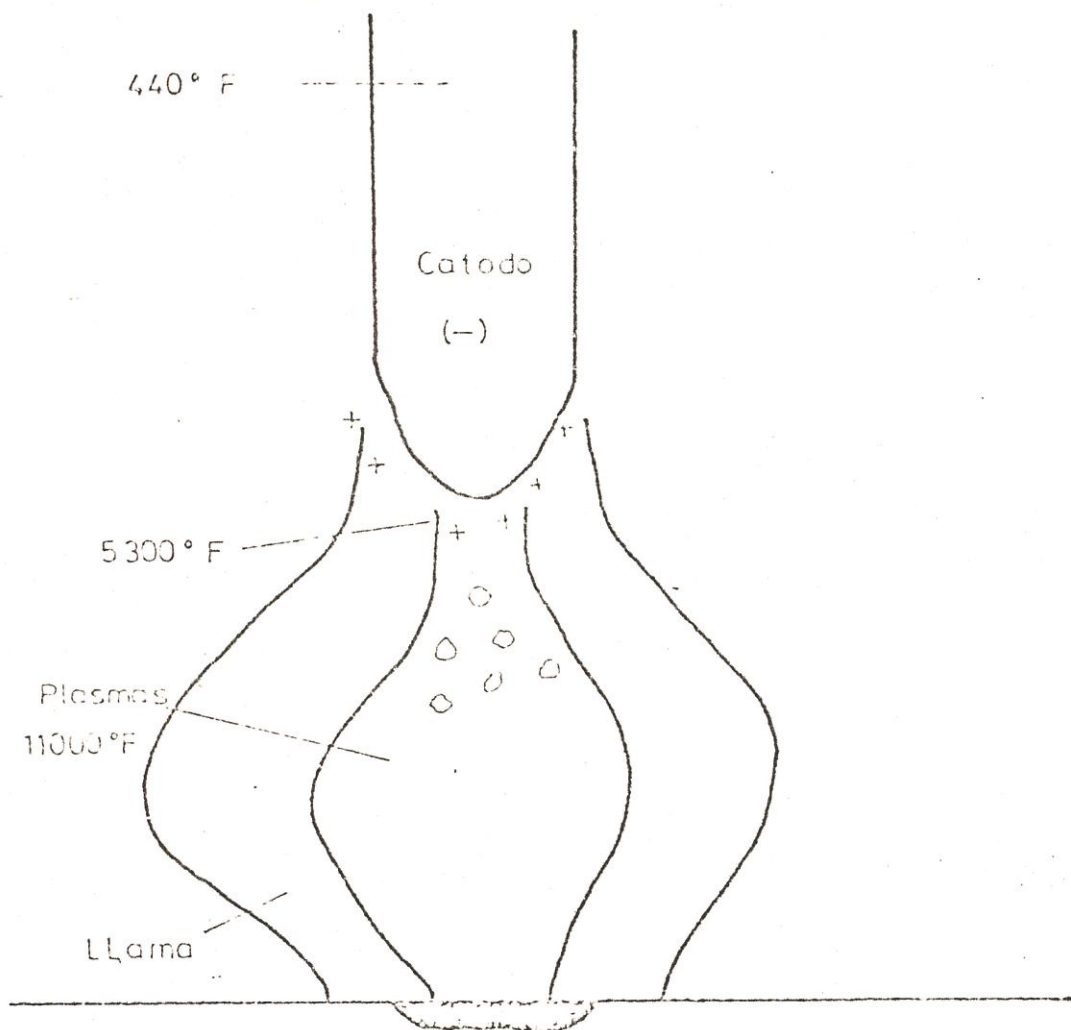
ARCO DE SOLDADURA ELECTRICO (14)
